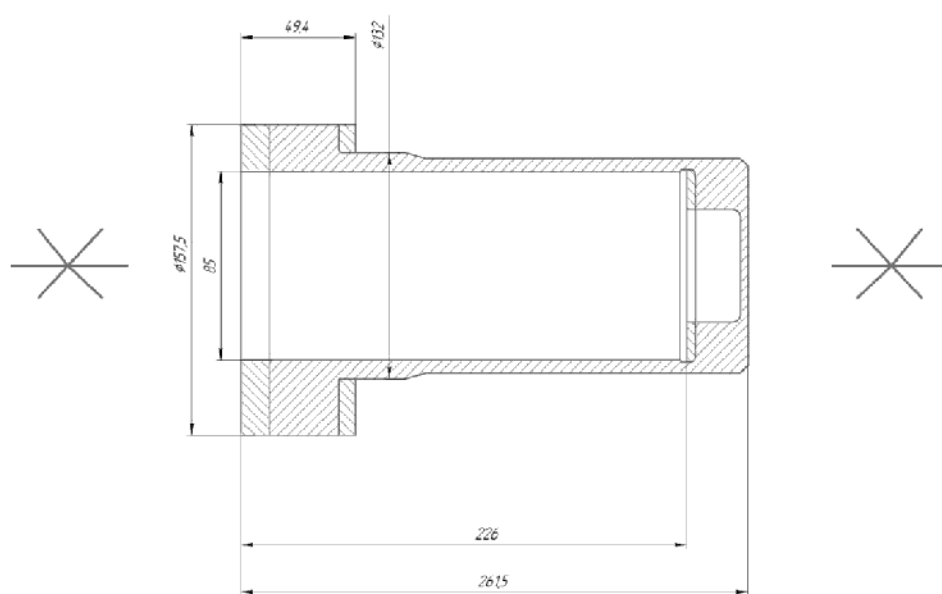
Ескіз заготовки в піщано-глинястій формі
